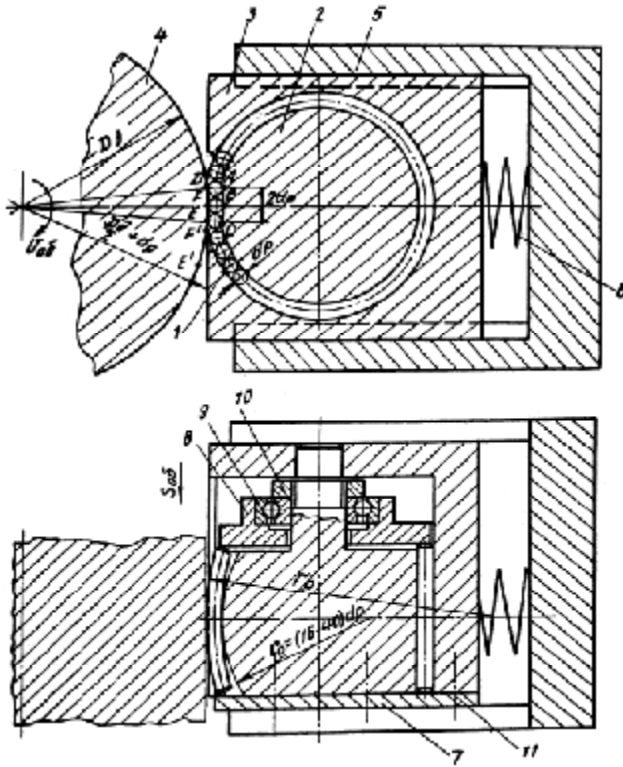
Устройство для чистовой обработки поверхностей тел вращения.
